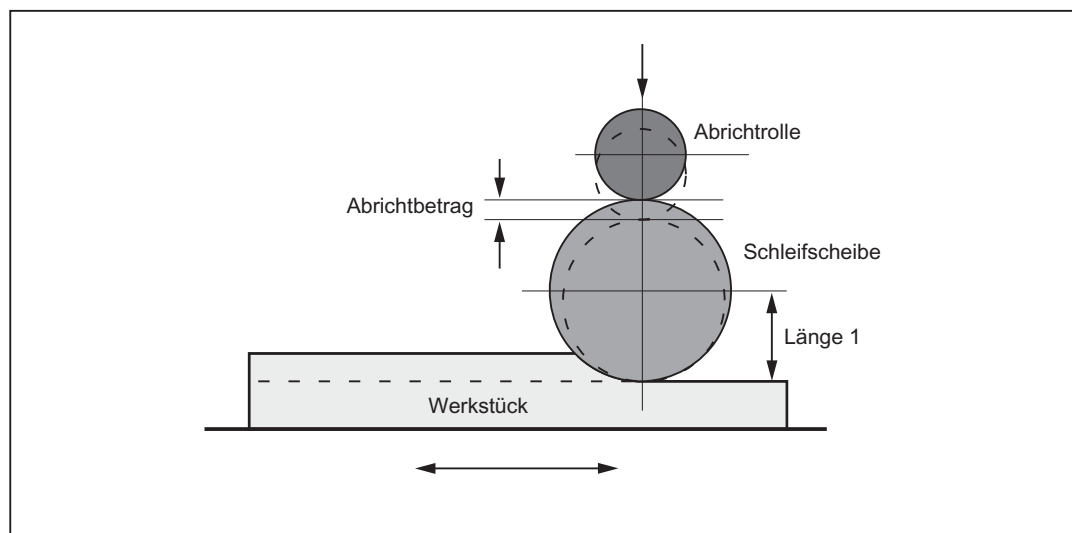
Abrichten während der Bearbeitung mit einer Abrichtrolle
